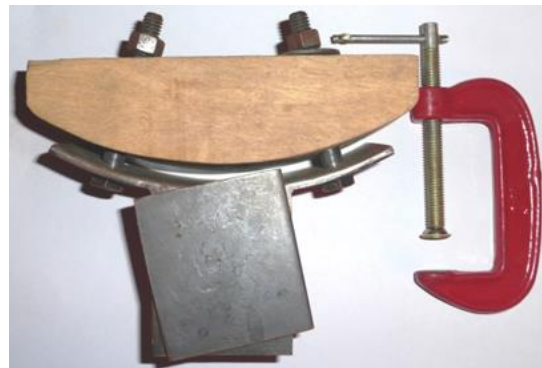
MOLDE DE SOPORTE DE TUBERÍA.
